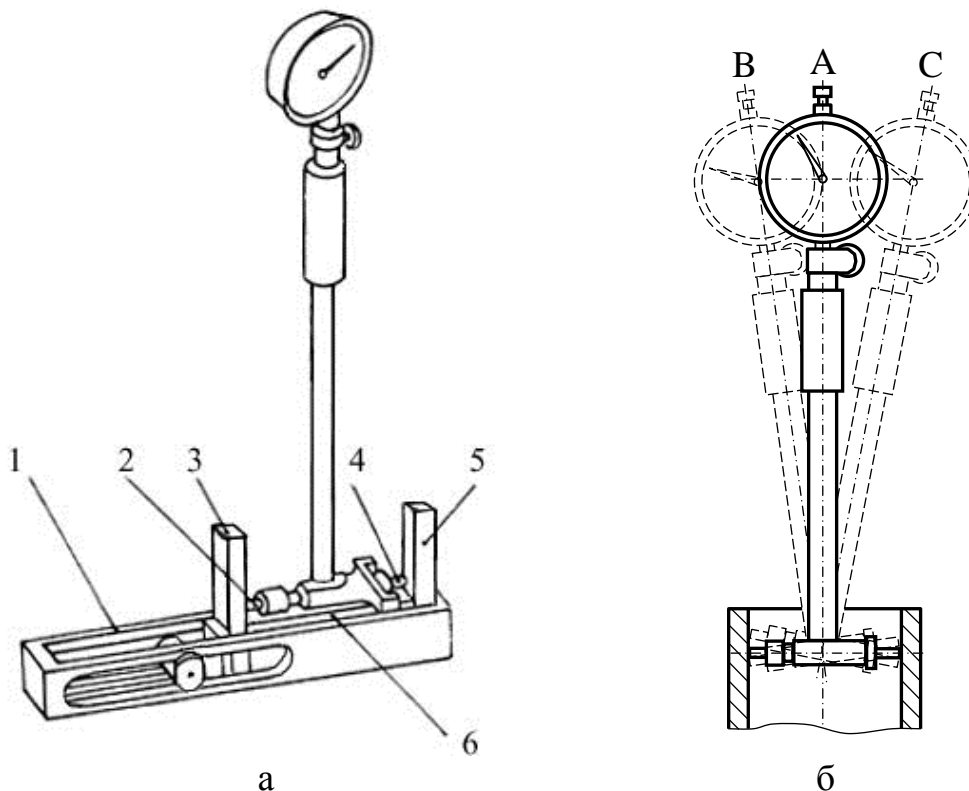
Схема настройки на эталонной размер (а) и установки в измеряемой детали (б) индикаторного нутромера: 1 – державка; 2 – измерительная вставка; 3, 5 – боковики; 4 – измерительный наконечник; 6 – блок концевых мер длины
